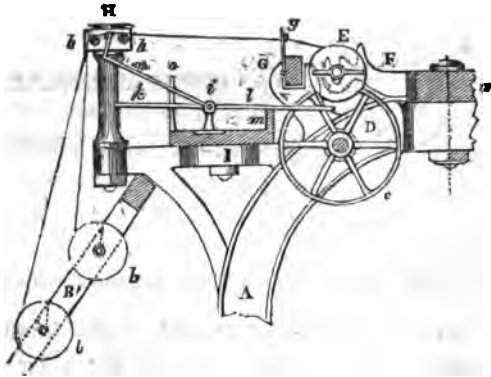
Mechanismus der Seidendoublirmachine. — Durchschnitt.
